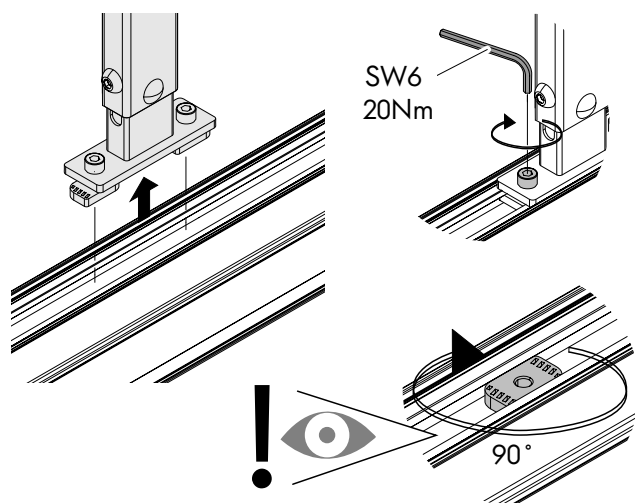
Montage du profilé à la fixation de suspension au plafond
